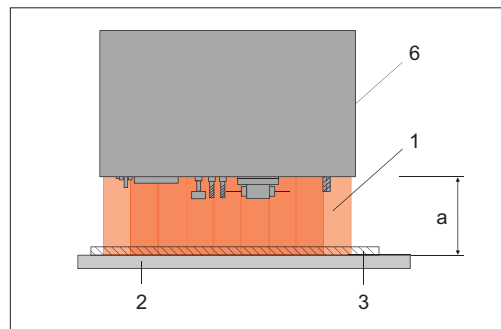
altezza massima (a) delle lamelle: 400 mm (corrisponde alla distanza massima tra riparo fisso e piano di appoggio del pezzo in lavorazione)
